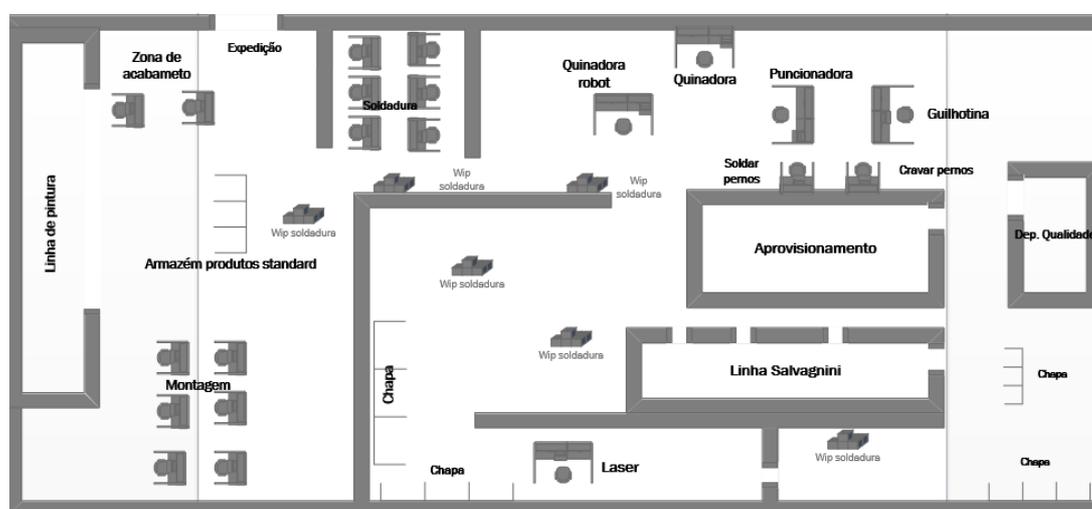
WIP* da soldadura espalhado pela área fabril
